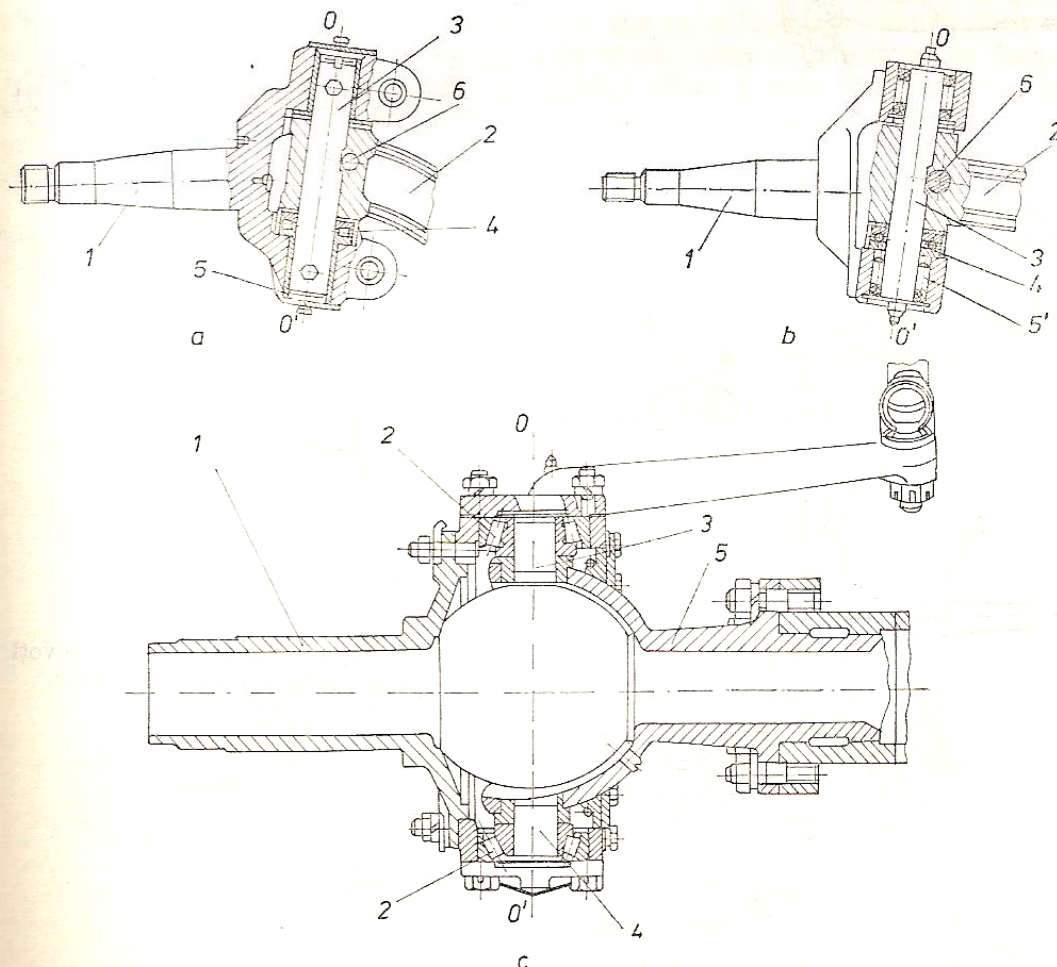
Tipuri constructive de pivoți și fuzete pentru punți rigide.
